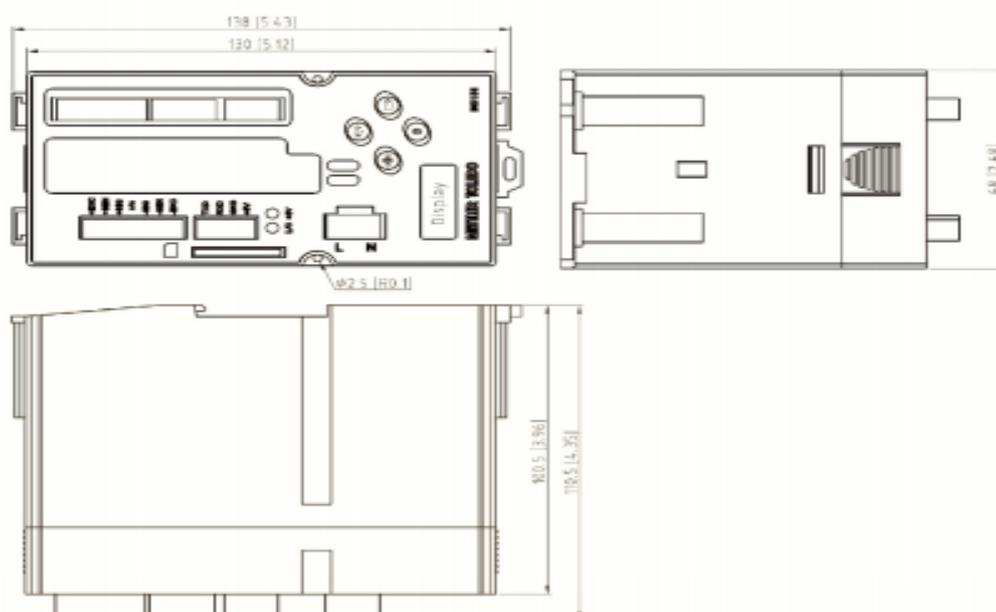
Dimensiones del gabinete de montaje en riel DIN de la IND131
